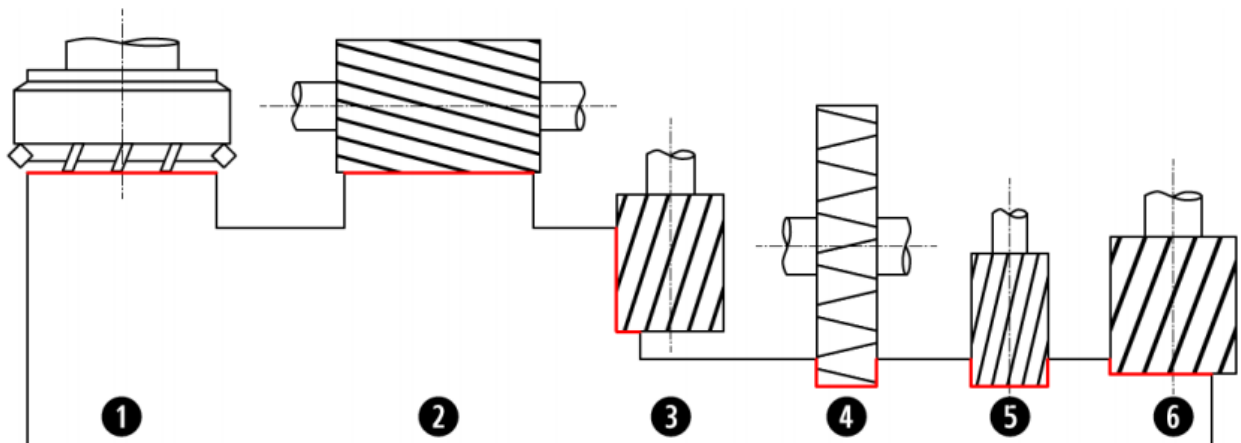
Opérations d'usinages en fraisage. [16]
